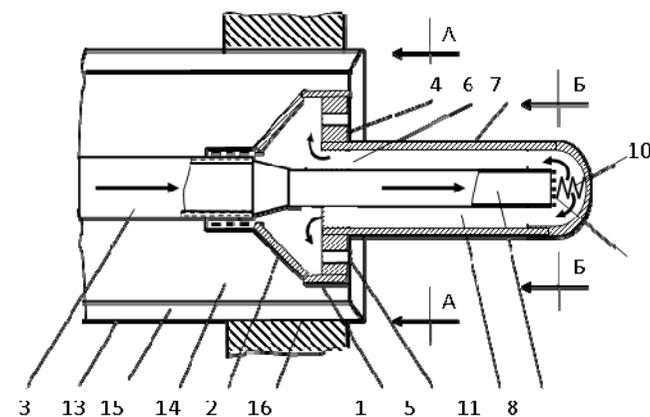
форсунка для горелки: 1-цилиндрический корпус; 2-днище; 3-топливоподающая трубка; 4-распылительная головка; 5-выпускные отверстия; 6-центральное отверстие; 7-нагревательная гильза; 8-выпускная трубка; 9-перфорированный клапан; 10-упругий элемент; 11-кольцевой циркуляционный канал; 12-полость цилиндрического корпуса; 13-корпус горелки; 14, 15-каналы первичного и вторичного воздуха; 16-амбразура топки
